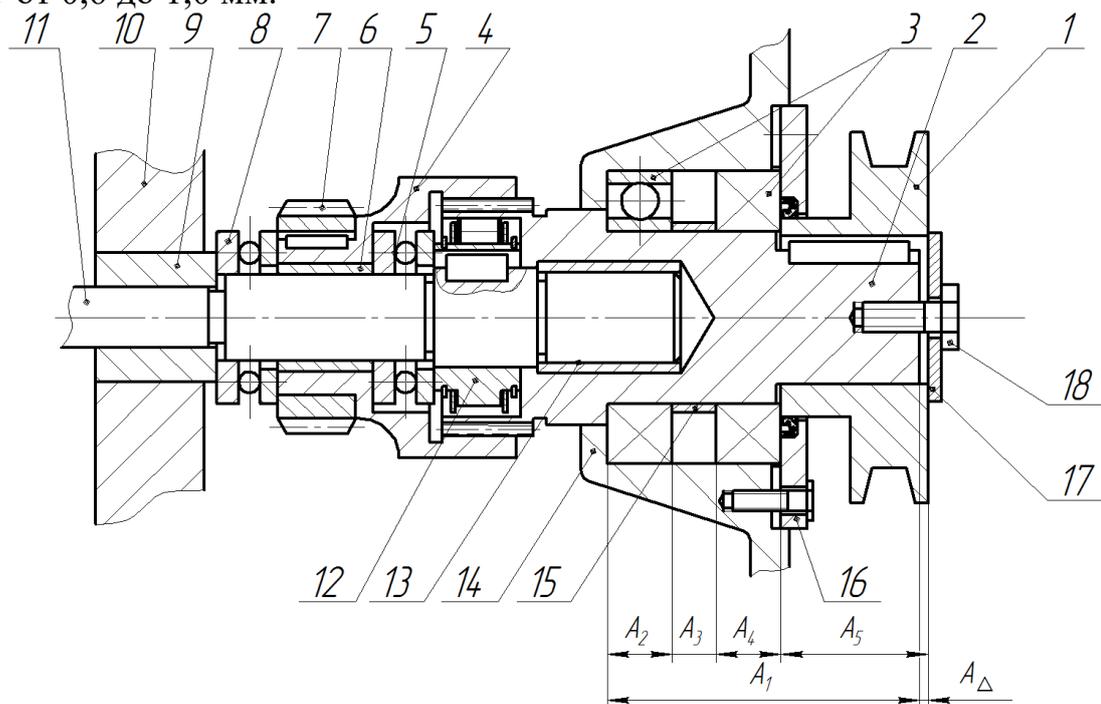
Общий вид сборочного узла. Схема размерной цепи.
